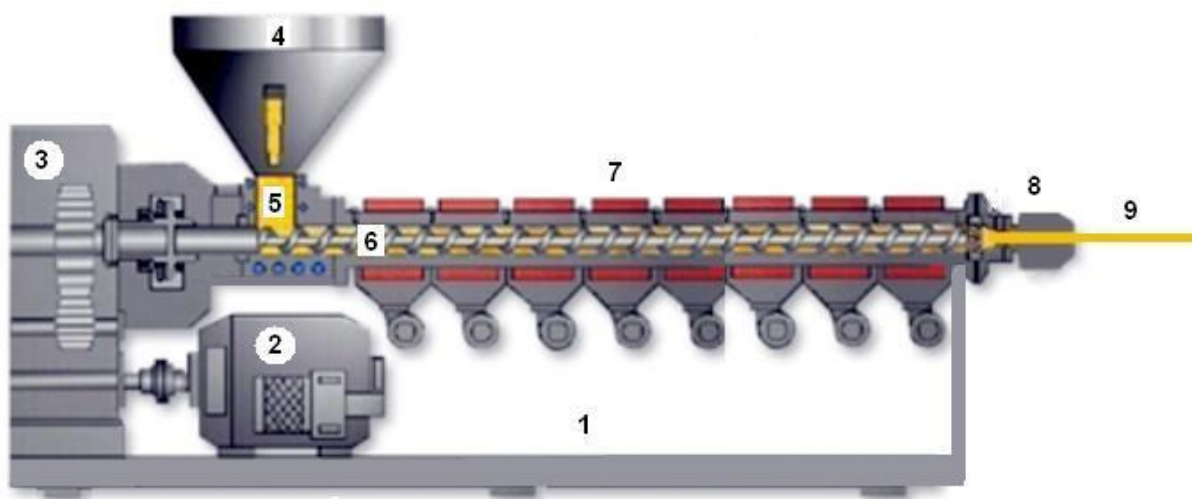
Стандартная схема одноцилиндрового экструдера: 1- станина; 2- электродвигатель; 3- редуктор; 4-бункер для гранулята; 5 –зона загрузки; 6- шнек; 7- корпус с элетронагревателями; 8- экструзионная головка;9 – экструдат
